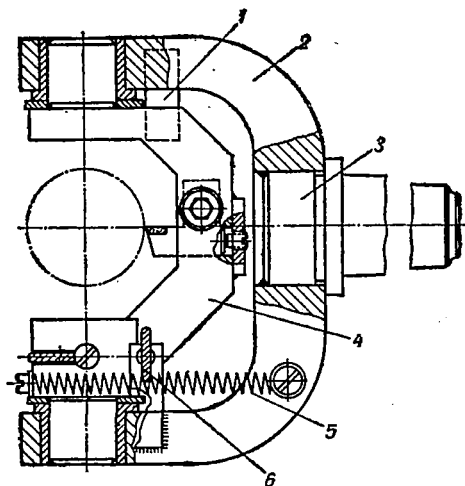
Приспособление к задней бабке станка для обточки сферических поверхностей.
